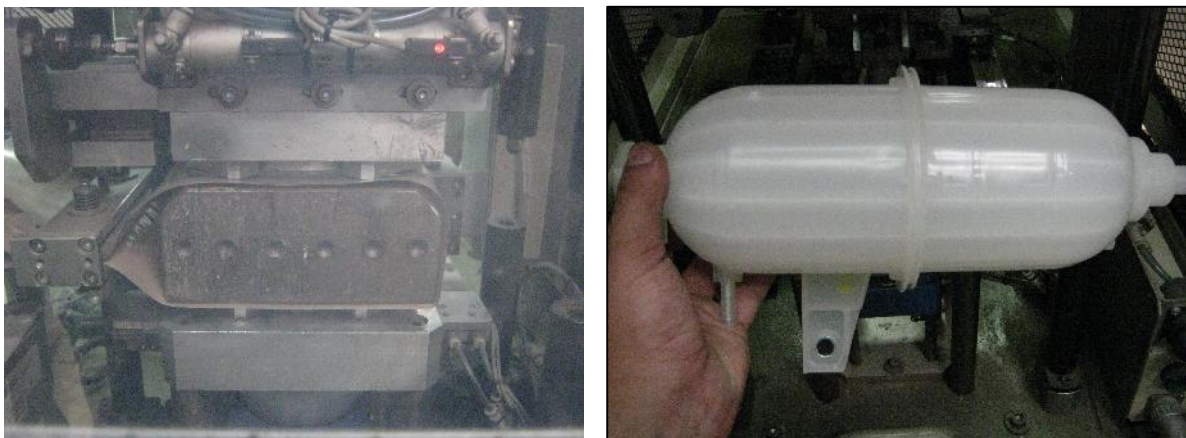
Operación de calentamiento y resultado luego de la soldadura
